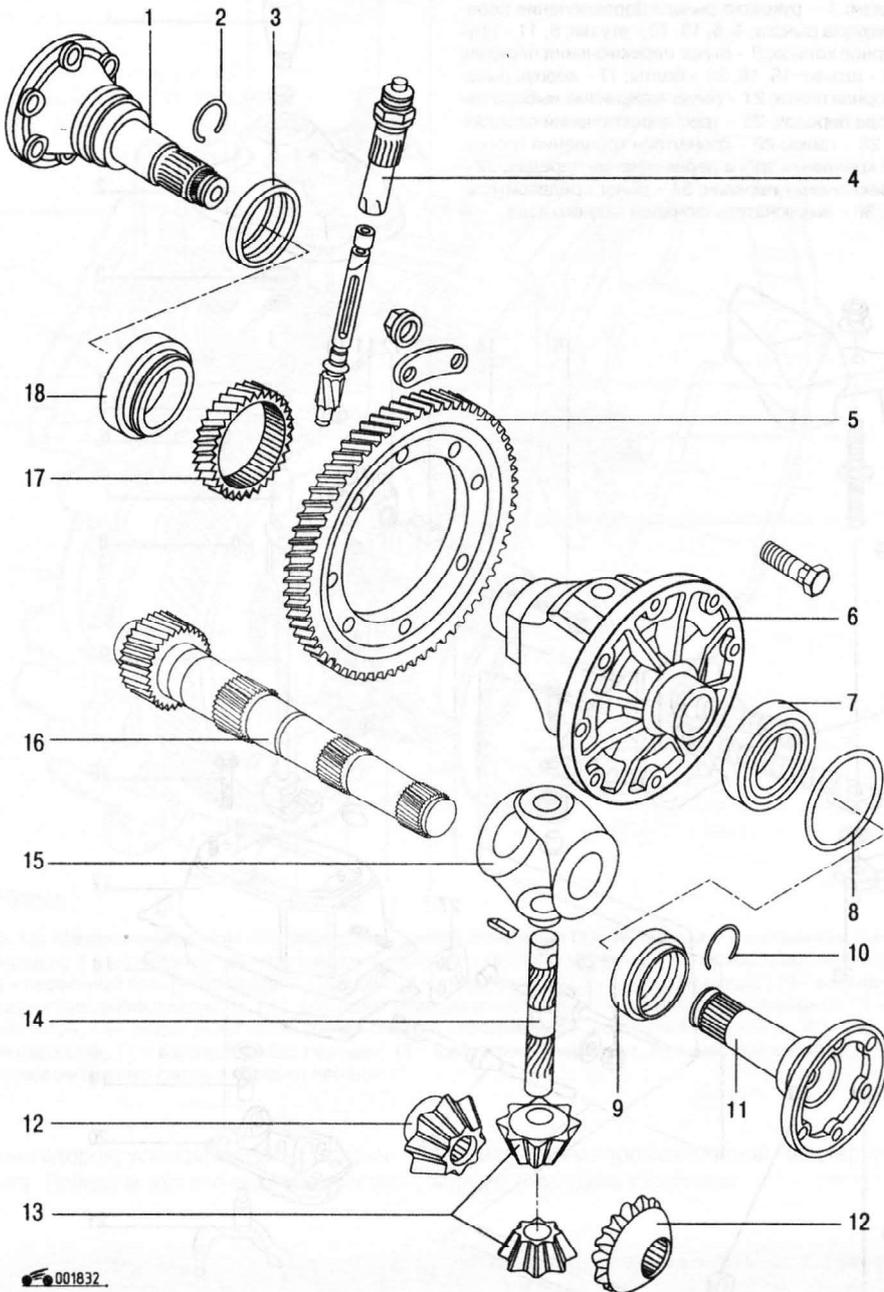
Главная передача и дифференциал: 1, 11 – фланцы полуоси; 2 – стопорное кольцо; 3, 9 – сальники; 4 – привод спидометра; 5 – ведомая шестерня главной передачи; 6 – корпус дифференциала; 7, 18 – подшипники дифференциала; 8 – упорная шайба; 10 – стопорное кольцо; 12 – полуосевая шестерня; 13 – сателлиты; 14 – ось сателлитов; 15 – сепаратор; 16 – вторичный вал; 17 – шестерня привода спидометра
